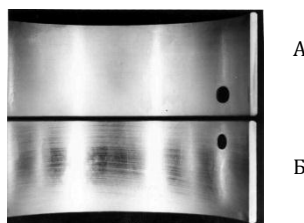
Рабочая поверхность вкладыша подшипника скольжения с эмульгатором 6СФК-180-0,5 (А) и без него (Б)
